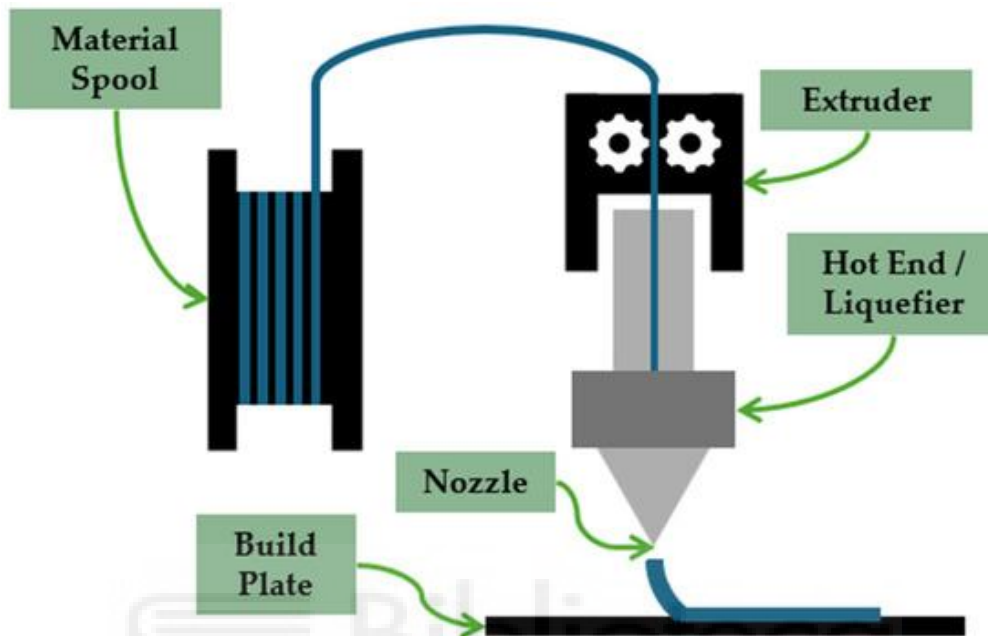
Esquema del proceso de impresión 3D por deposición fundida (FDM) [5].
